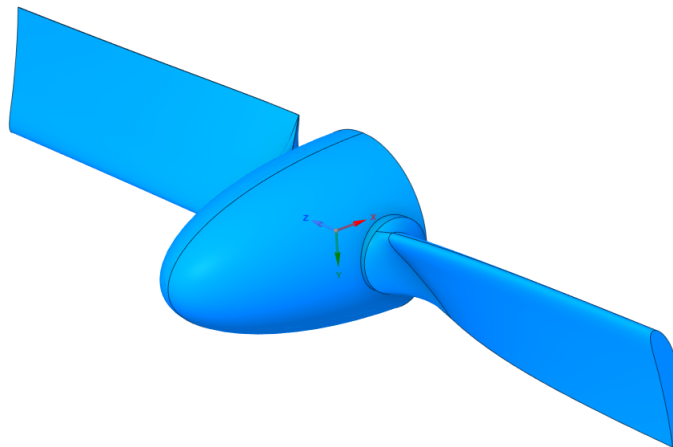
Diseño CAD del rotor de la turbina RAT.
